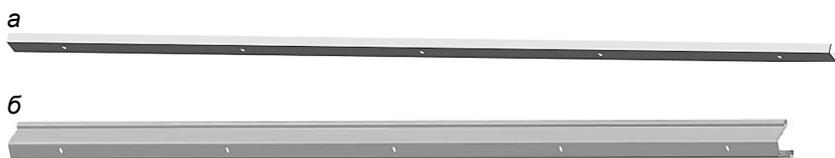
Жесткий подхват: а – швеллер; б – спецпрофиль
